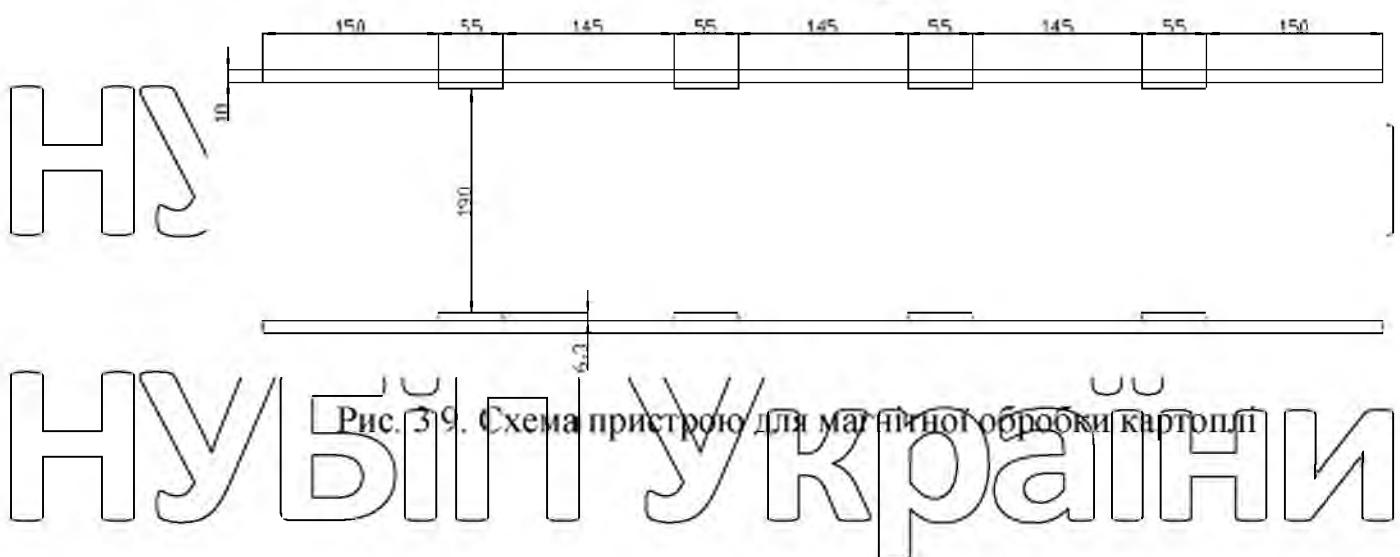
Схема пристроя для магнітного обробки картоплі
